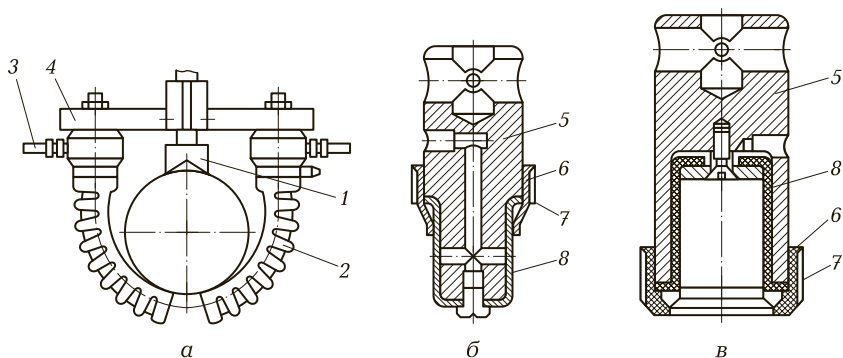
Захватные устройства с изгибающейся (а) и расширяющейся (б, в) камерами:
